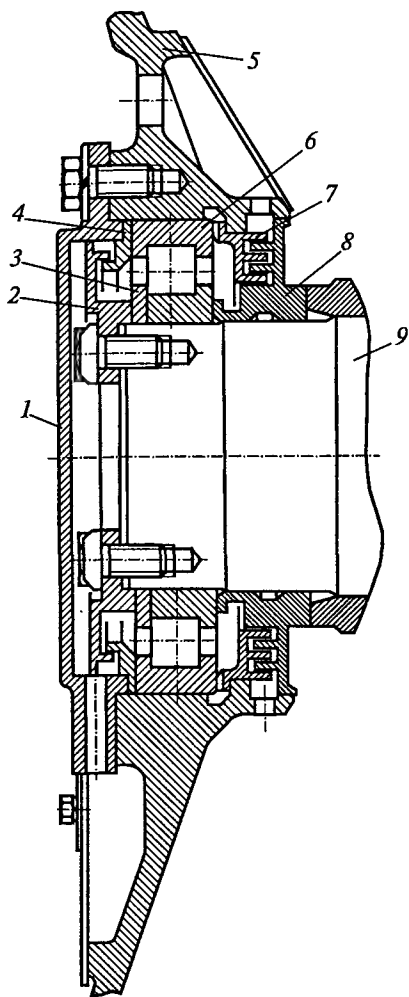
Малый подшипниковый щит электродвигателя ДТК-800КЭ:
